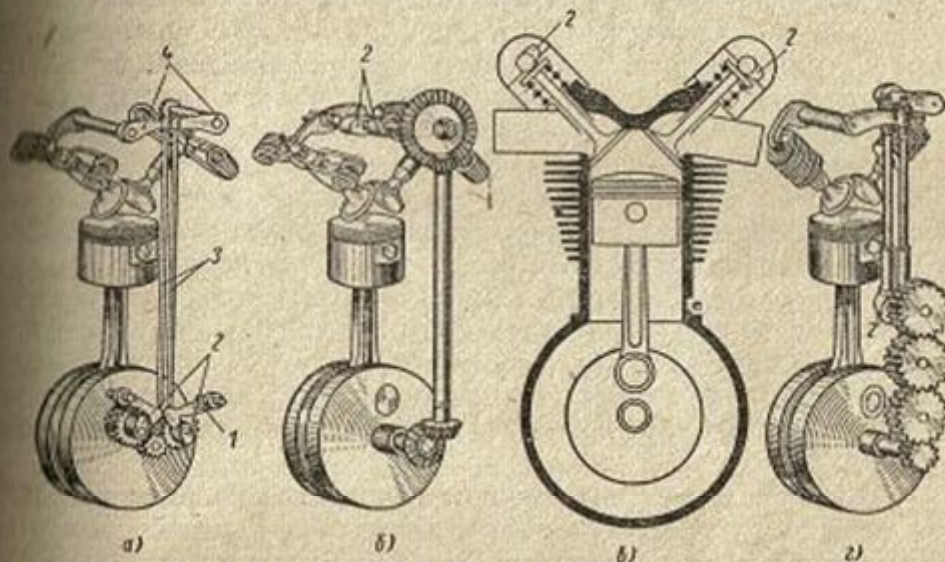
Расположение распределительного вала у верхнеклапанных двигателей:
